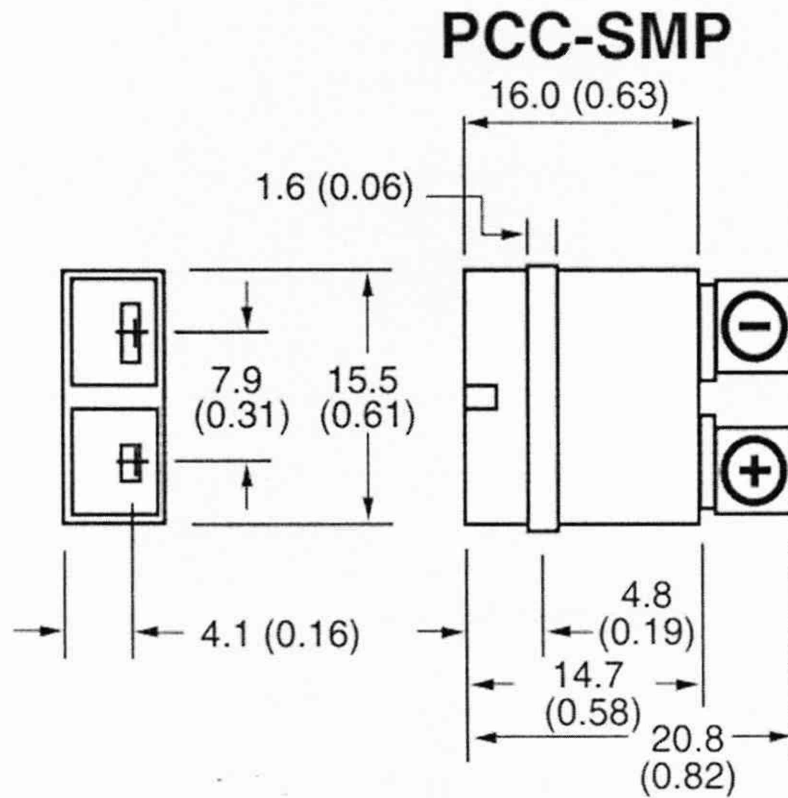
Внешний вид входного миниатюрного соединителя ВТ-96 PCC-SMP-U
